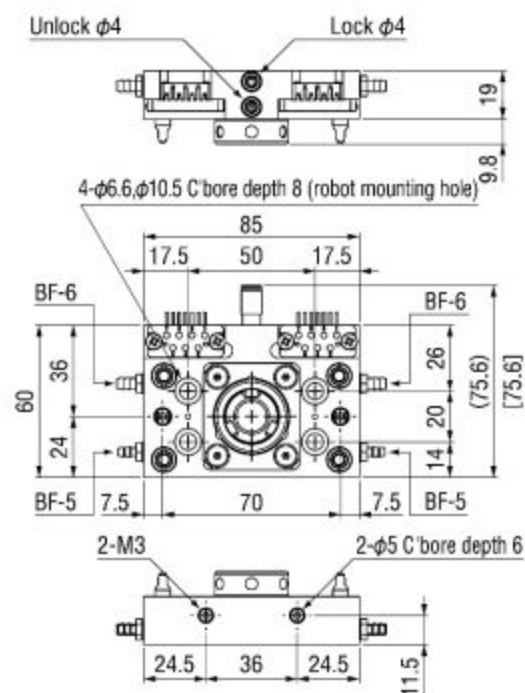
Dimensões do acoplador ligado a cabeça do robô [33].
